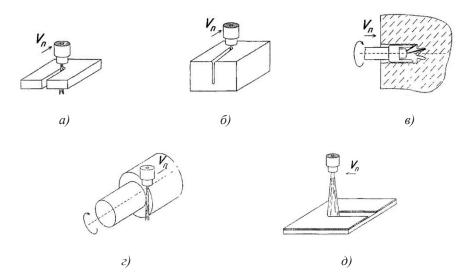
Схема гидроабразивной резки: a — разрезание; δ — нарезание несквозных щелей; ϵ — бурение; ϵ — точение; δ — очистка
